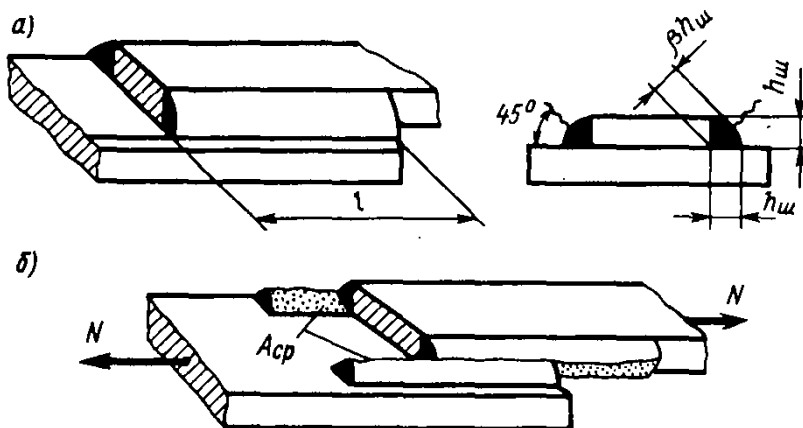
Угловые швы сварного соединения работают на срез
